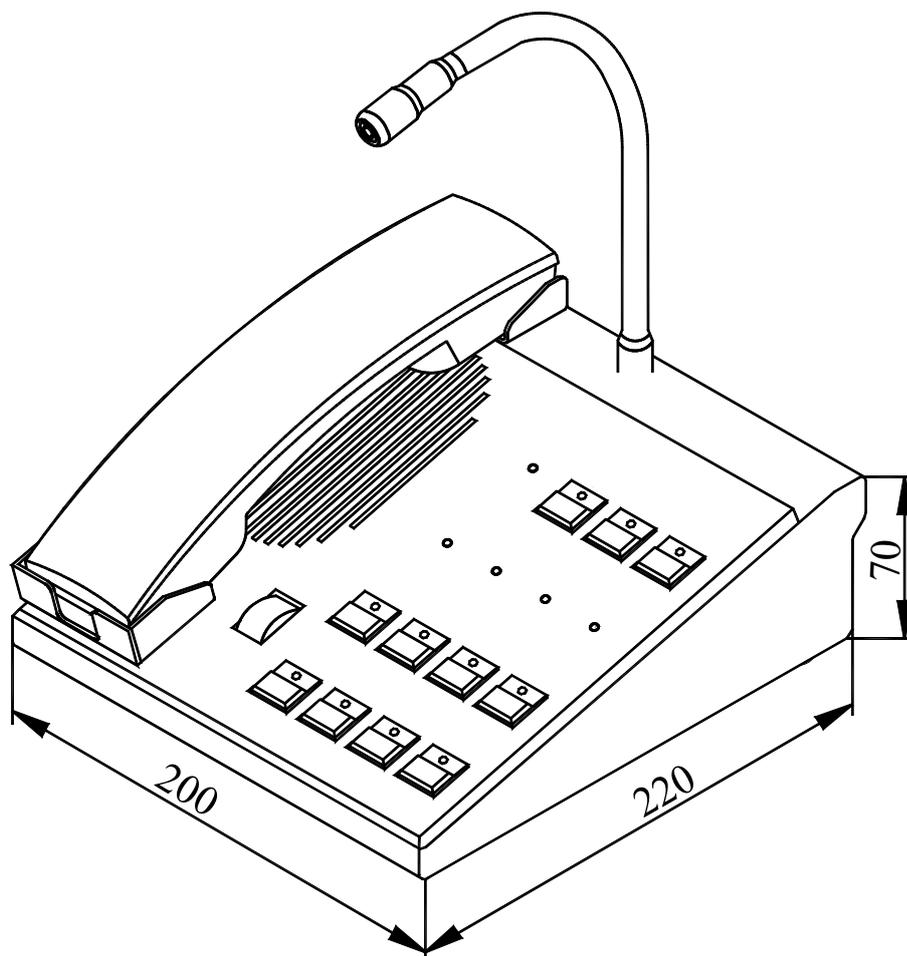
Внешний вид и габаритные размеры ПР.У
